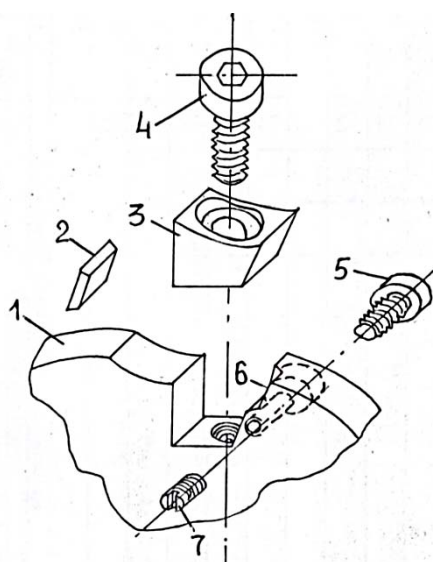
Узел крепления пластины трехсторонней дисковой фрезы E51
